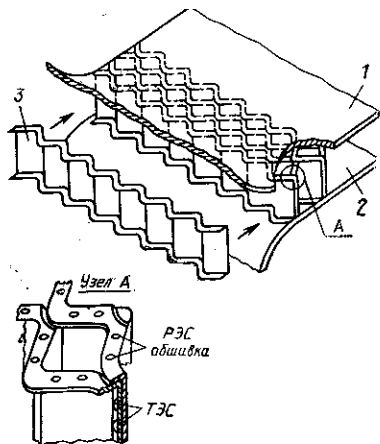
Схема сборки сварных панелей по методу фирмы «Стресскин»: 1, 2 — обшивка панели; 3 — ленточка гофрированной фольги сотового заполнителя
